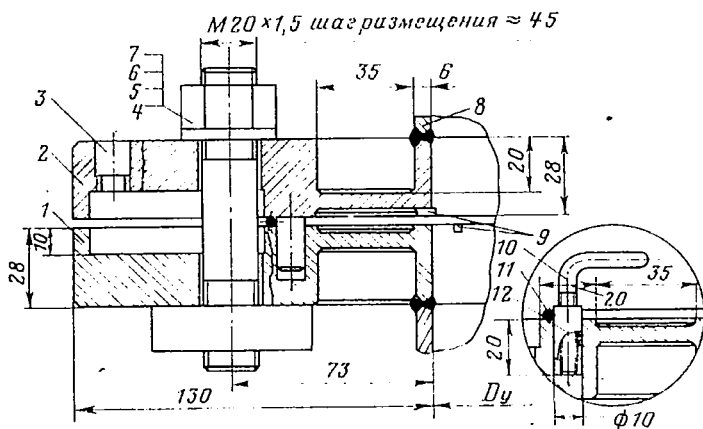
Конструкция и размеры фланцевых венцов для проволочного уплотнения крупногабаритных соединений.
